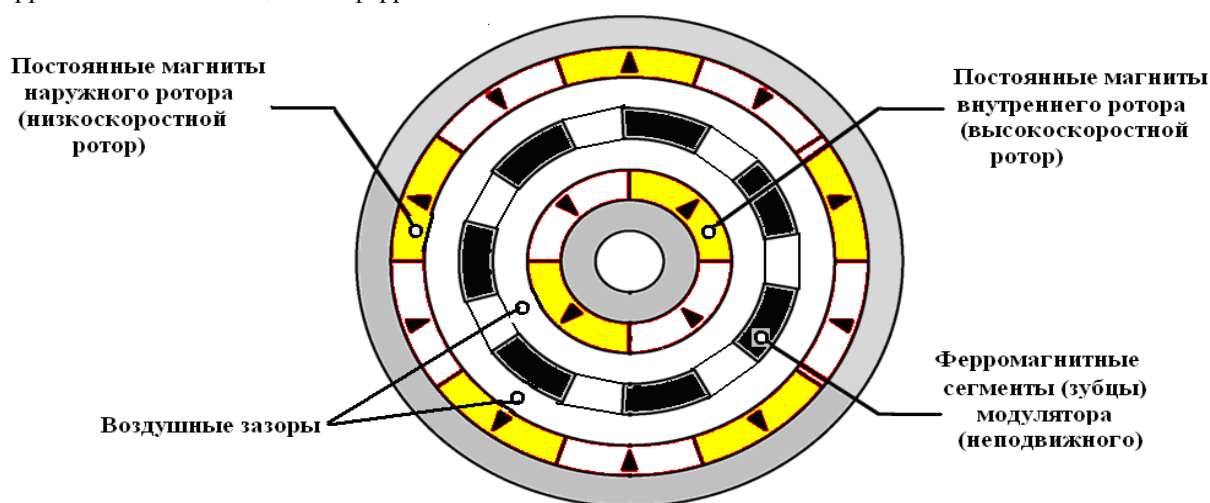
Поперечный разрез одноступенчатого цилиндрического редуктора.
